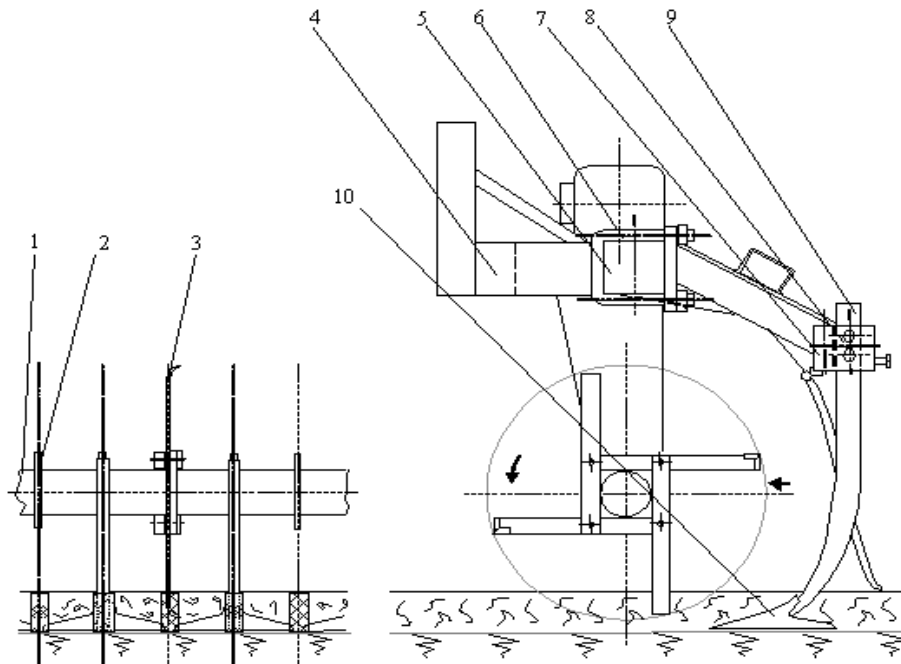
Конструктивна схема модернізованої фрези з комбінованими робочими органами:
